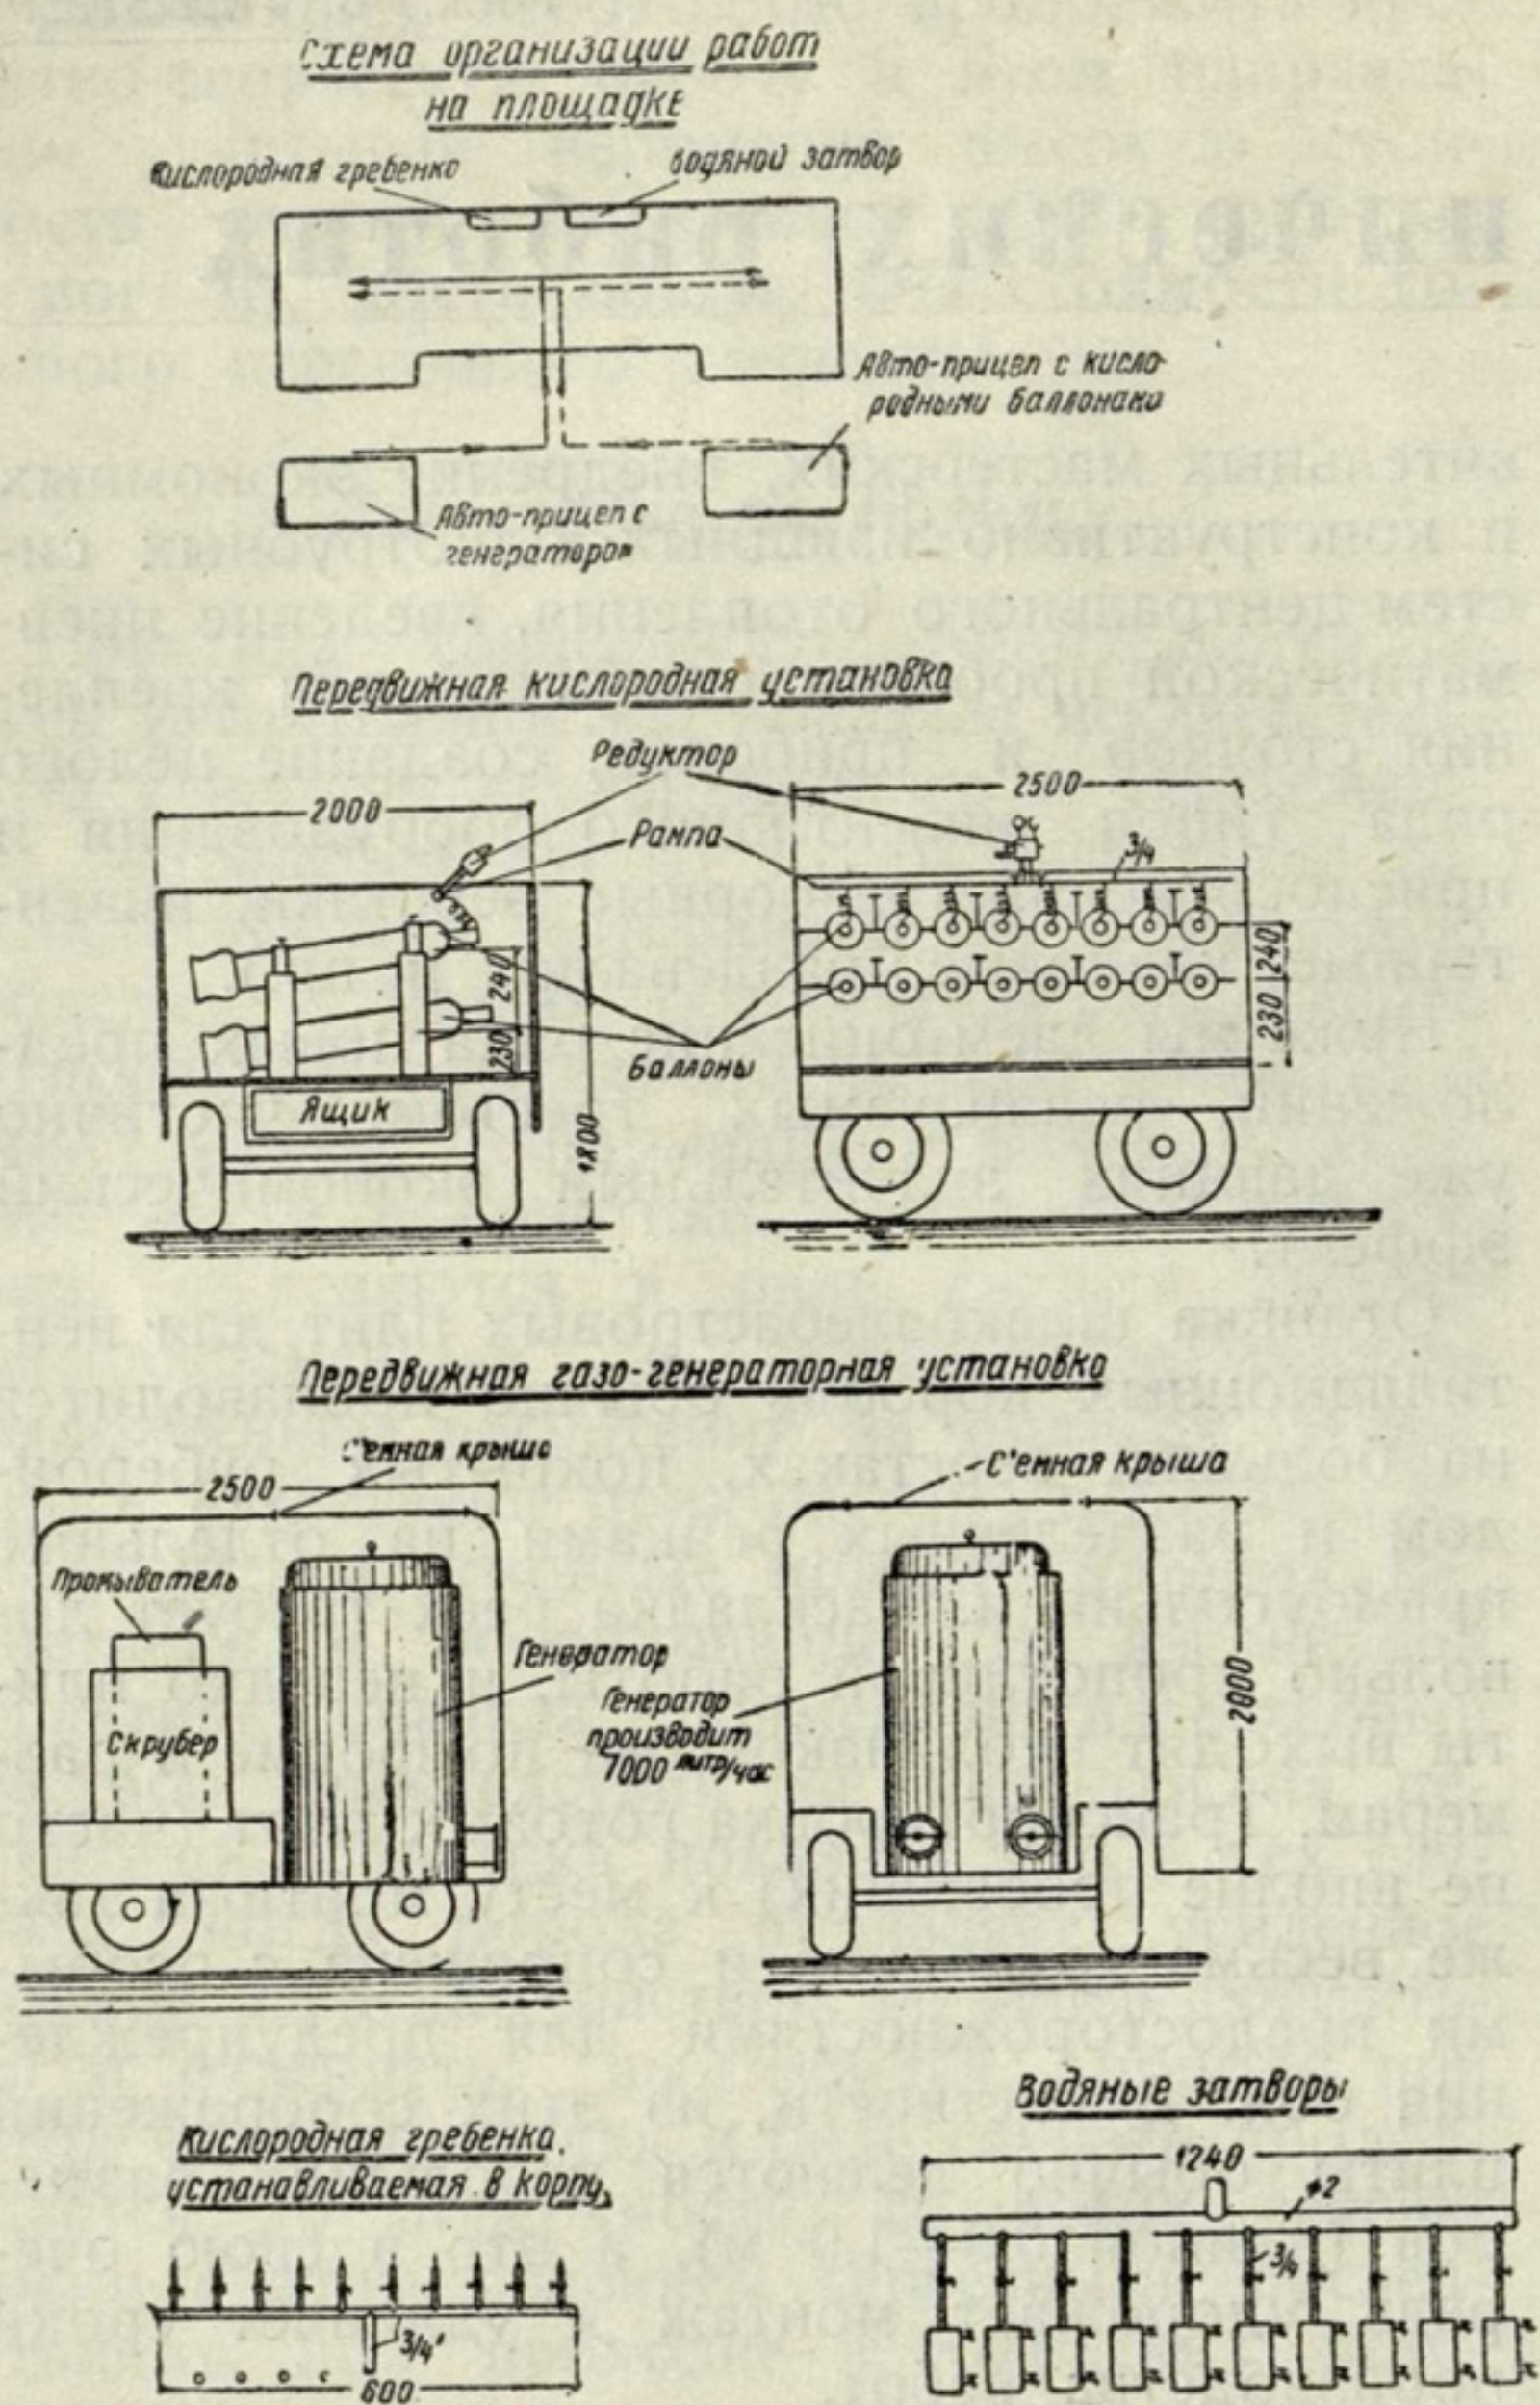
Передвижная газосварочная установка на 8—10 одновременно работающих горелок.
